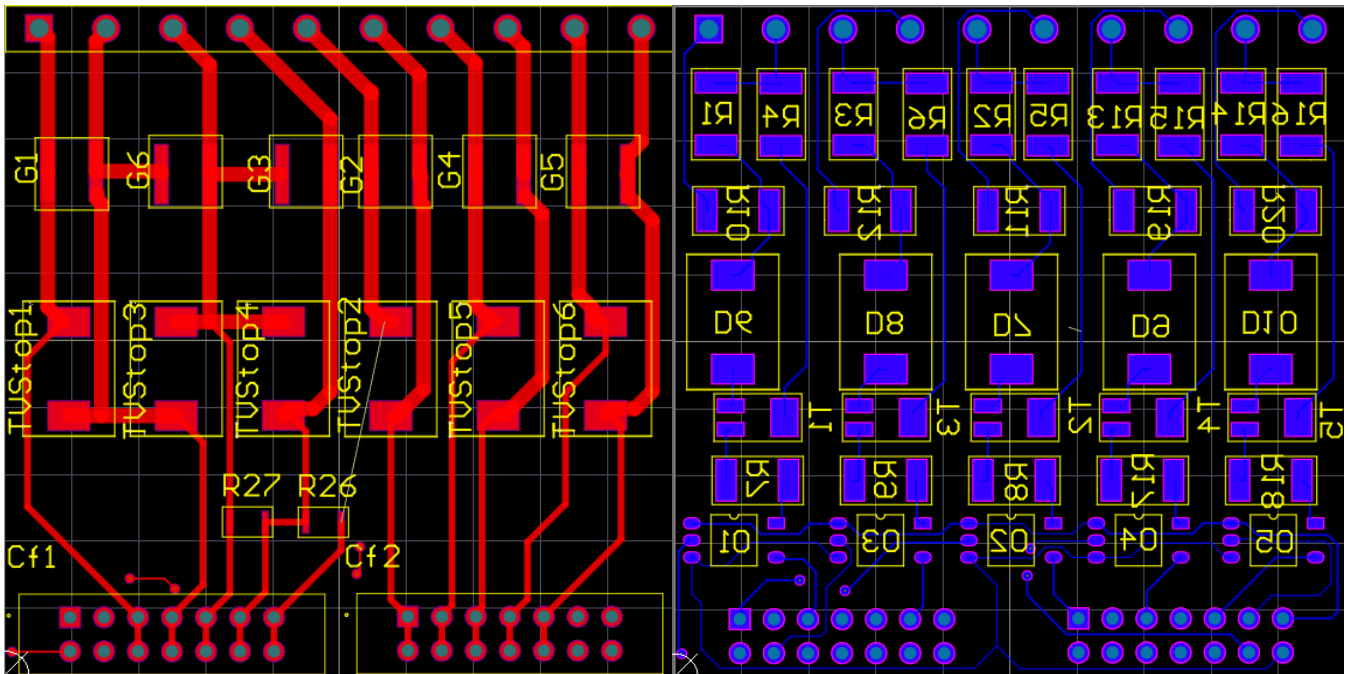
top layer(rosso) e bottom layer (blu) della pcb
